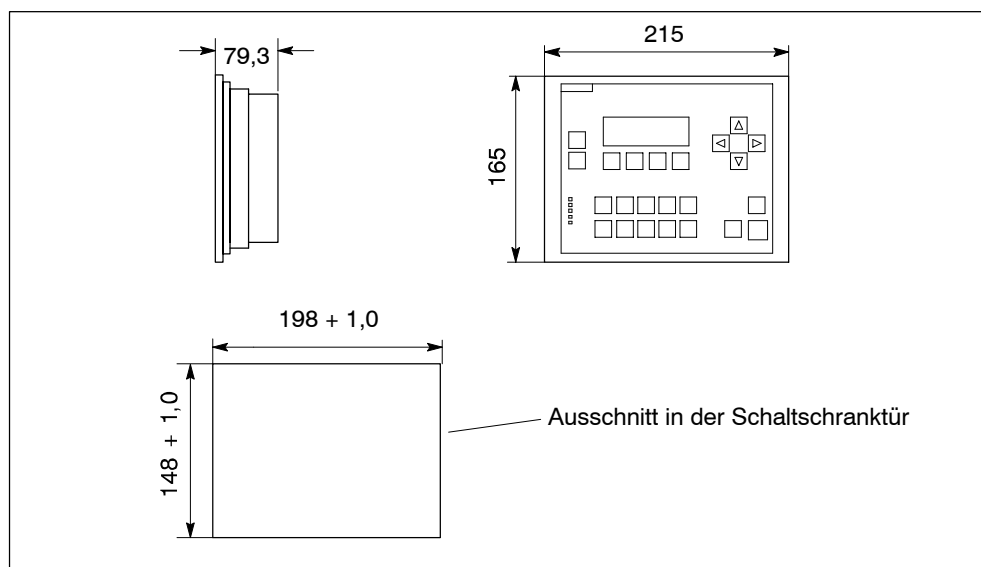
Maßbilder für das C7-613 (Maße in Millimeter)
